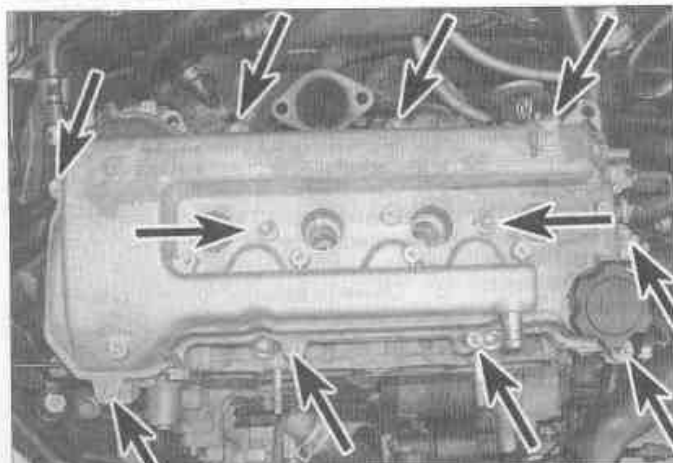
Болты/гайки/шпильки крепления крышки головки цилиндров
